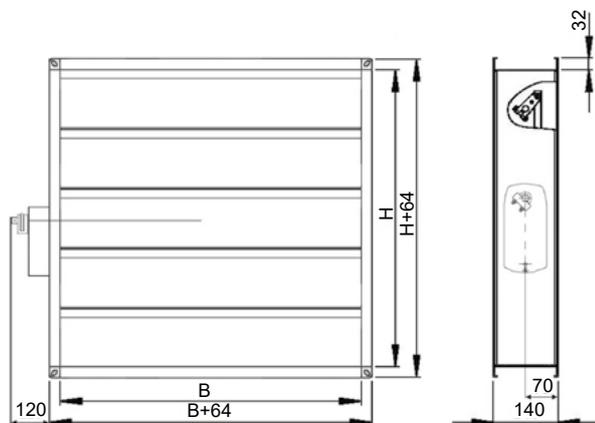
Размеры TORNE-S с площадкой под привод (M0). Ручка поставляется в комплекте, снимается перед установкой привода.
